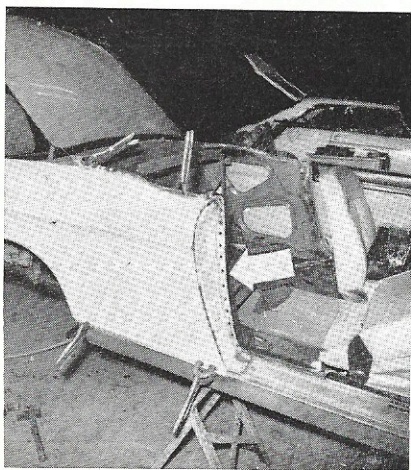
Soudage d'entrée de porte sur armature de côté arrière.
